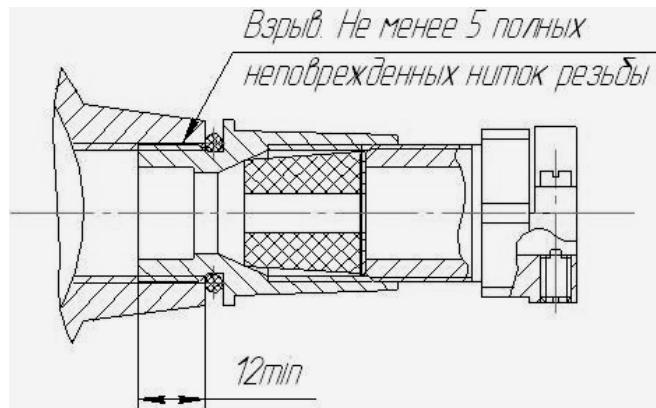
А. Чертеж средств взрывозащиты ввода бронированного кабеля с зажимом для металлорукава (маркировка взрывозащиты 1ExdIIBT6)
